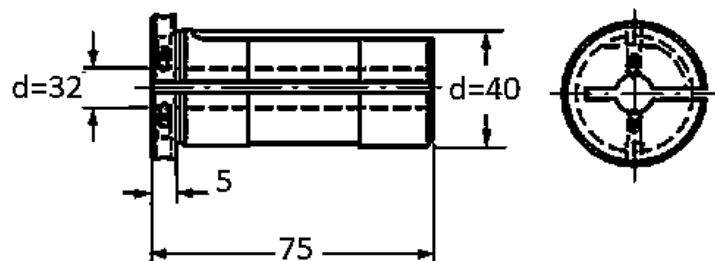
Цилиндрическая втулка для подрезного резца 132N-4032
